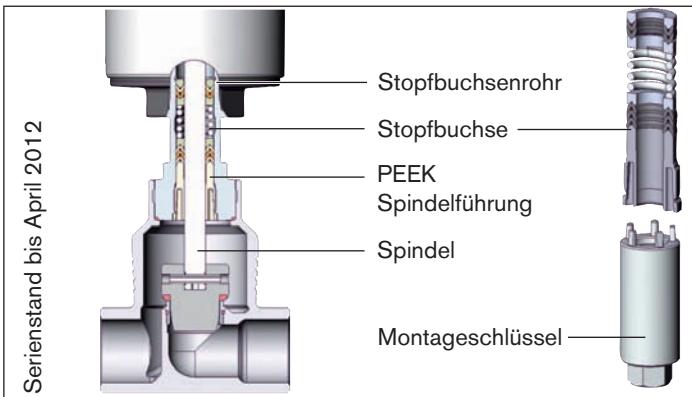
Austausch Stopfbuchse (PEEK Spindelführung)
